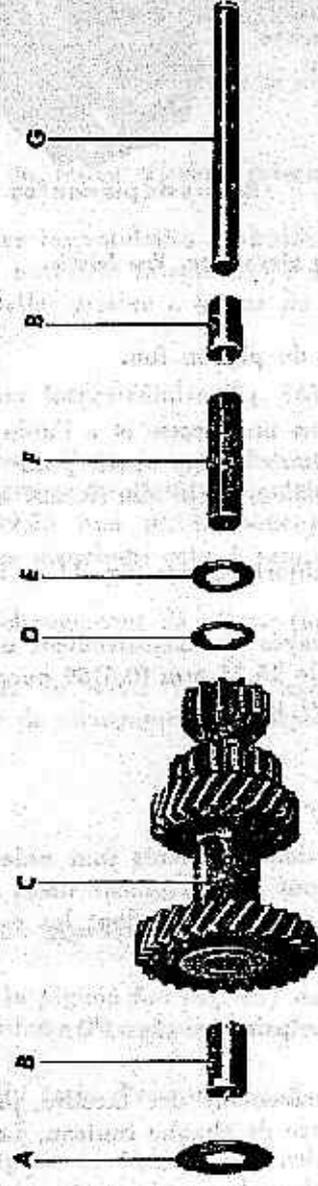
Train d'engrenages de l'arbre intermédiaire. Vue éclatée
